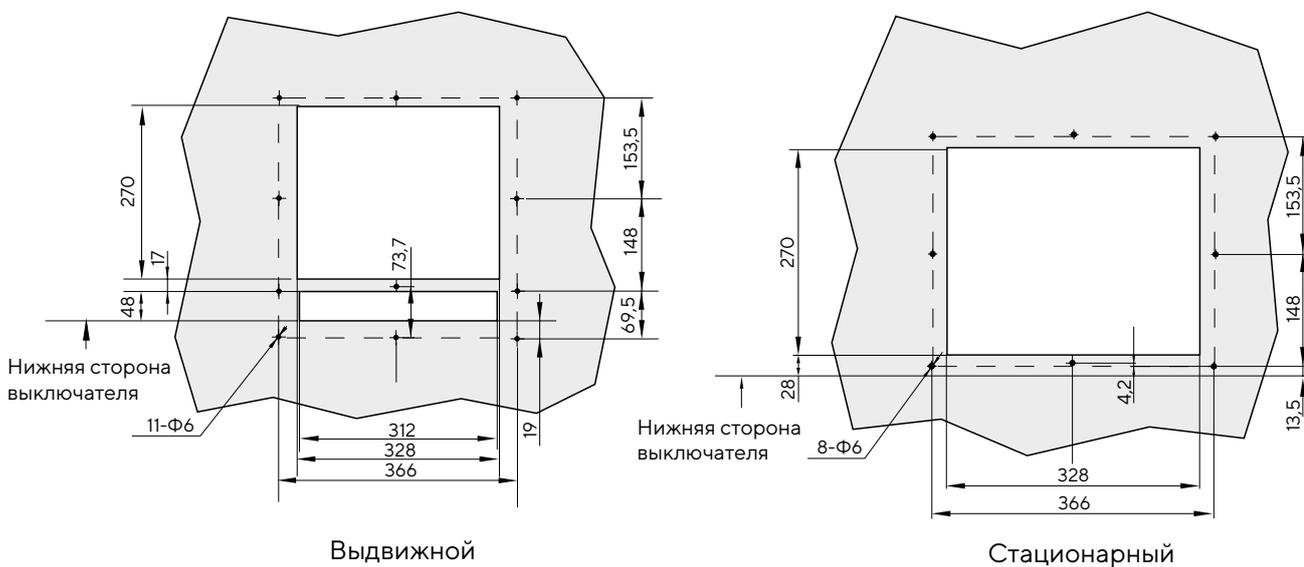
Габаритные размеры рамки обрамления выреза в двери для выключателей типоразмера F
